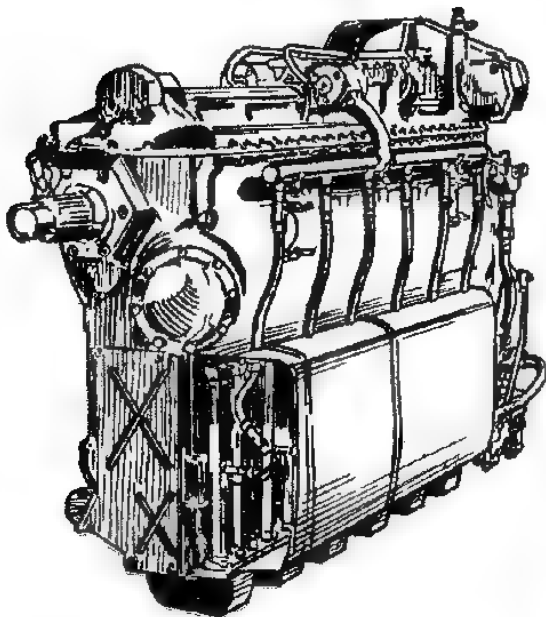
Motor a explosión con 6 cilindros en línea de la *De Havilland*.
